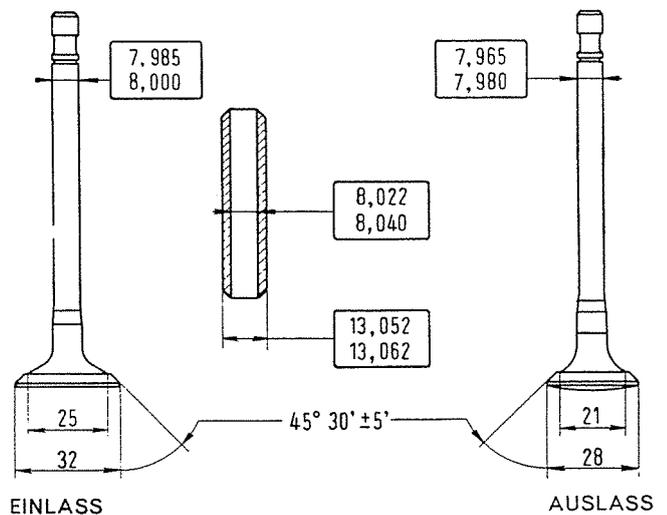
Hauptabmessungen der Ventile und ihrer Führungen.
